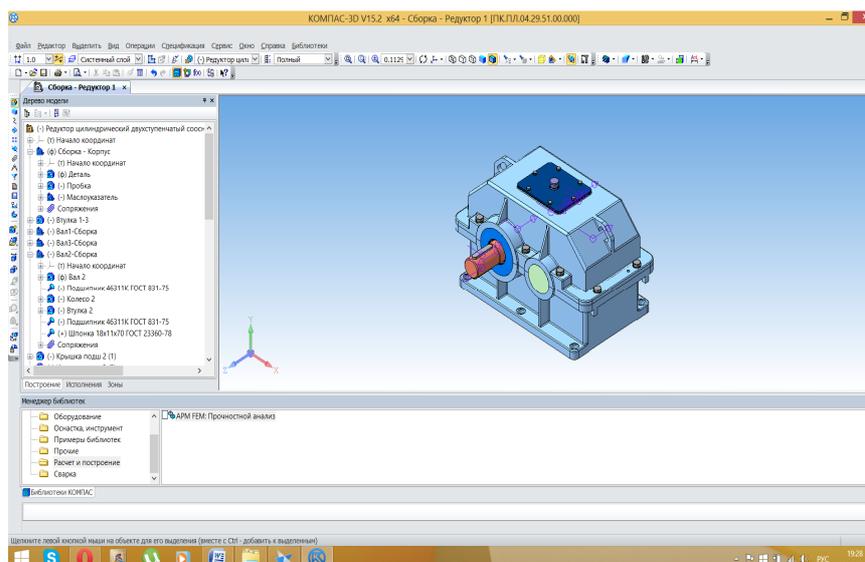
3D модель двухступенчатого цилиндрического соосного редуктора в COMPAS-3D
